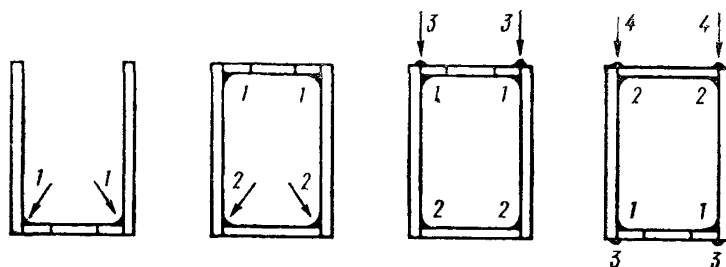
Последовательность наложения швов при сварке коробчатых элементов двухдуговым автоматом
